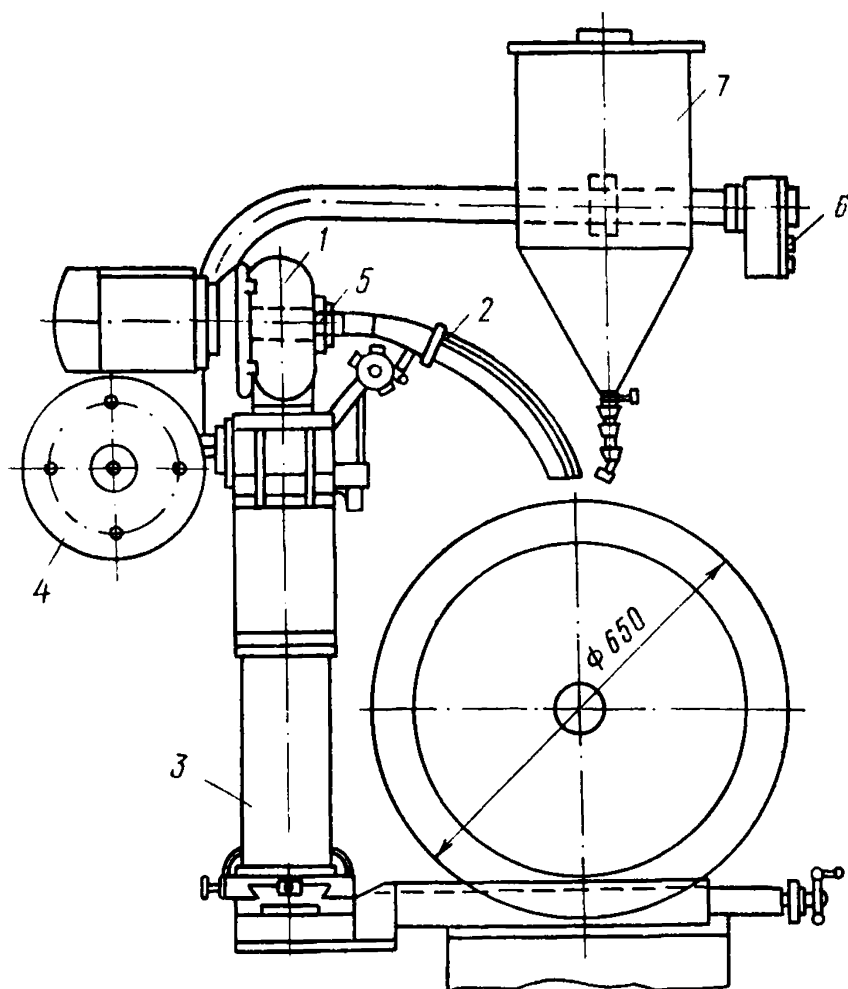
Схема установки для наплавки тел вращения под слоем флюса:
